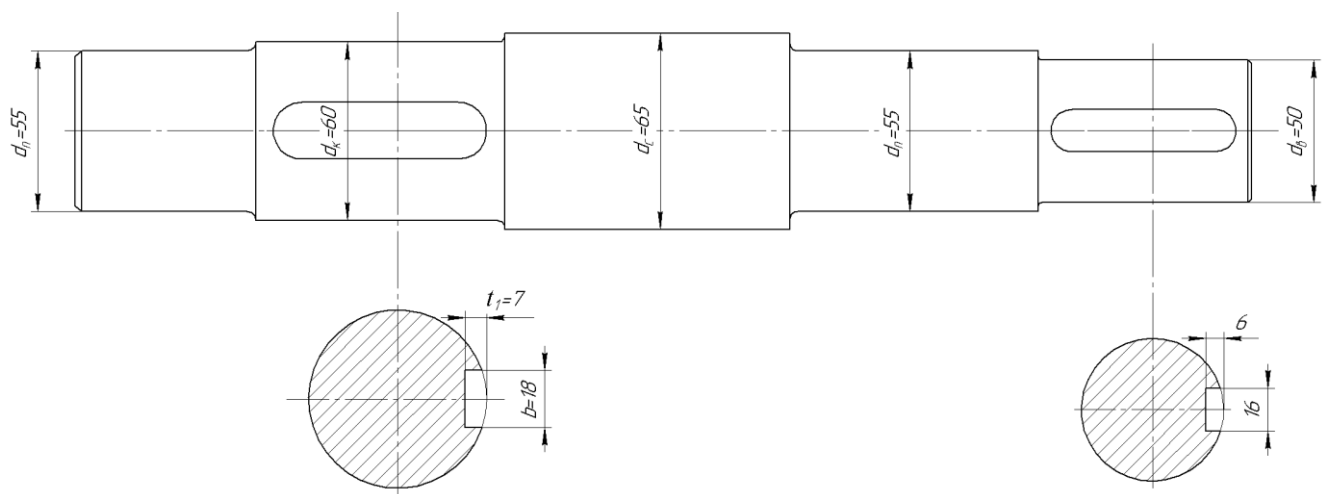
Конструкция вала с увеличенными размерами сечений
